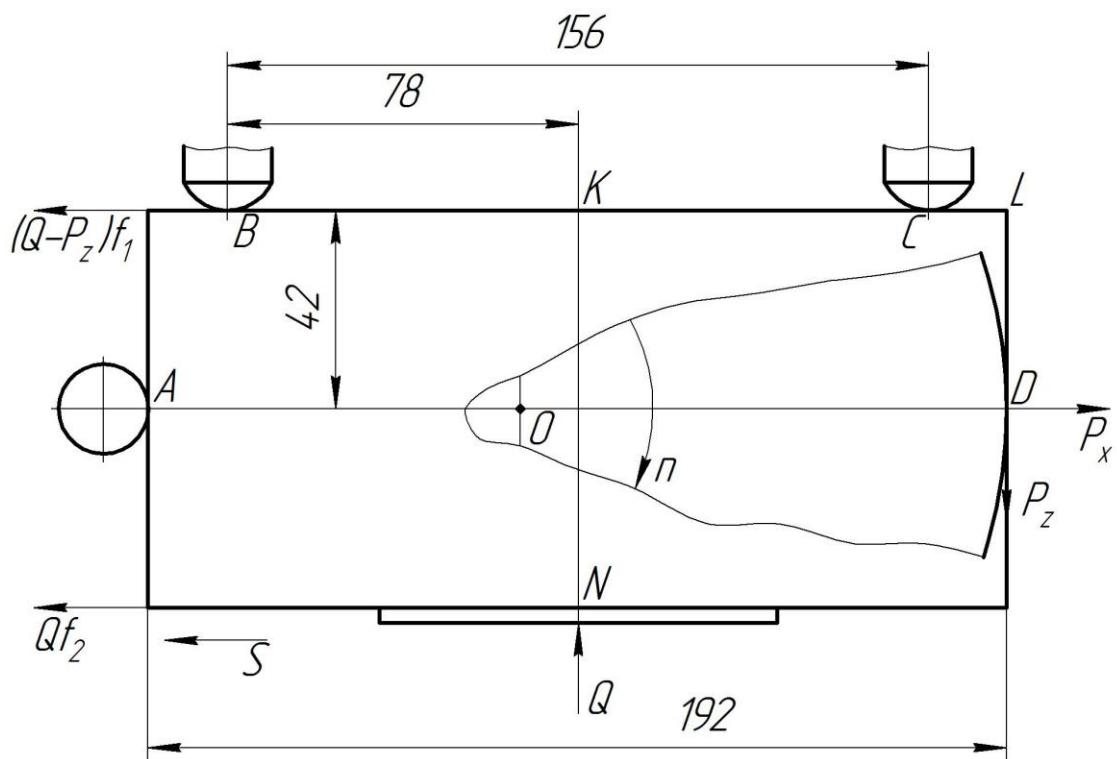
Схема до розрахунку сили заліску заготовки при фрезеруванні площини
